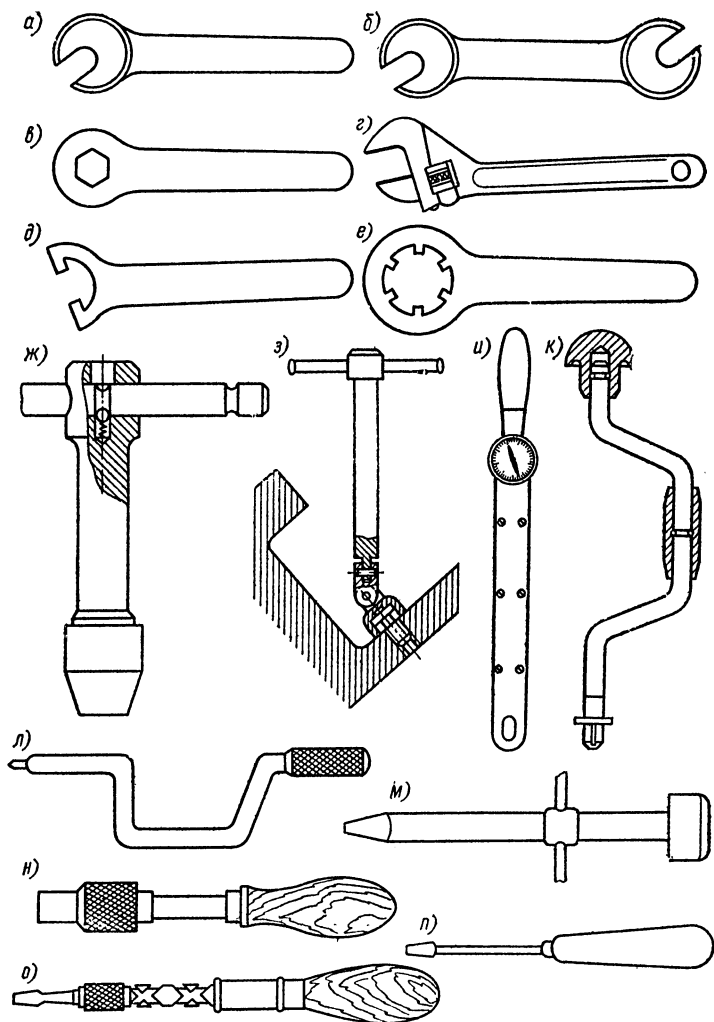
Ручной инструмент для сборки резьбовых соединений
